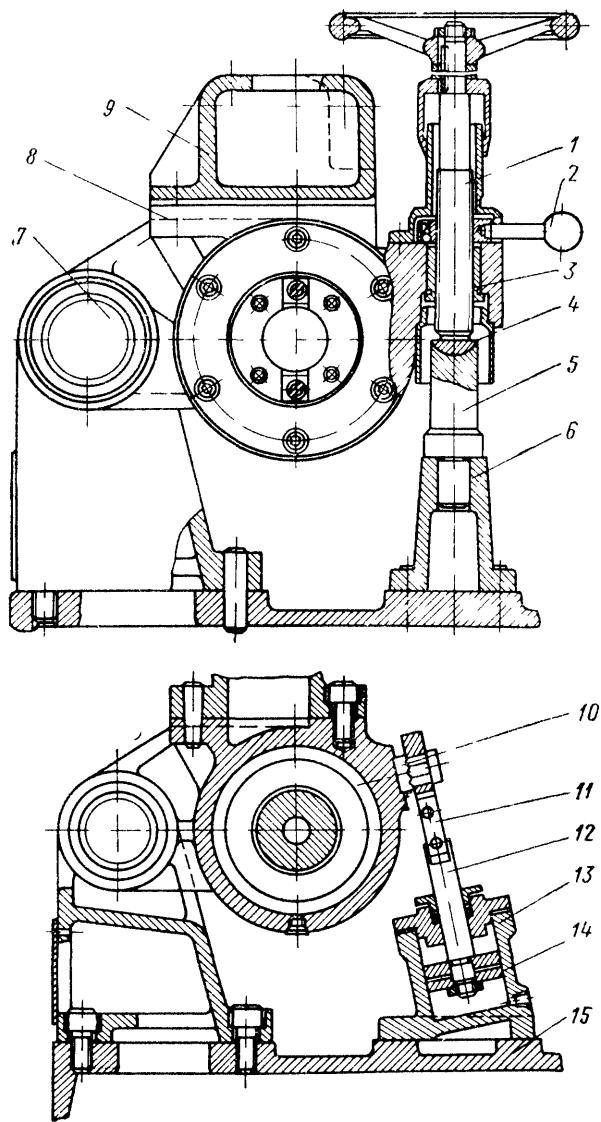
Фрезерная бабка полуавтомата модели 6В2
